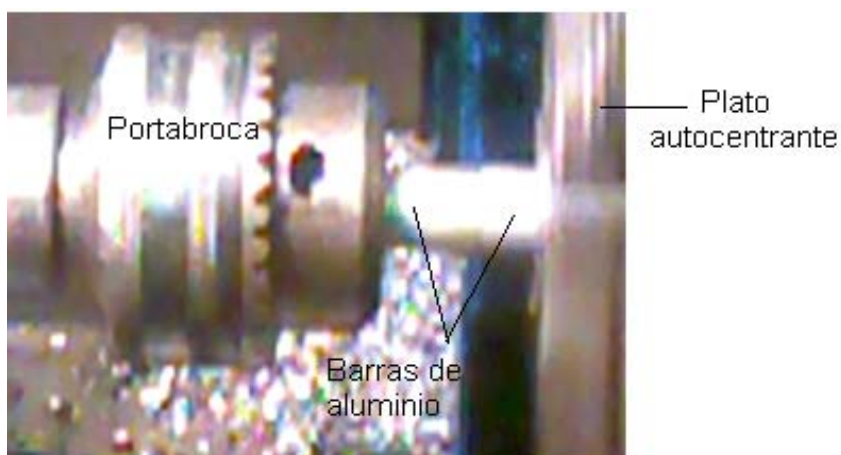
Instalación del proceso de soldadura a tope de la aleación de aluminio.
